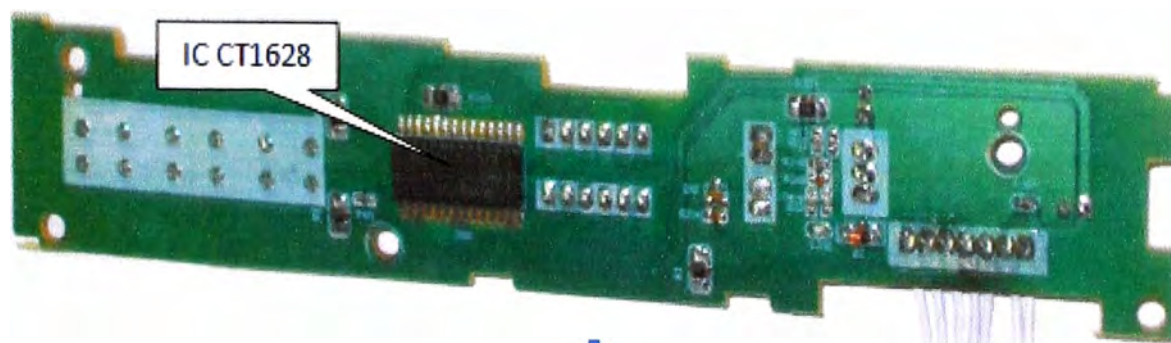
Panel frontal (lado soldadura)
